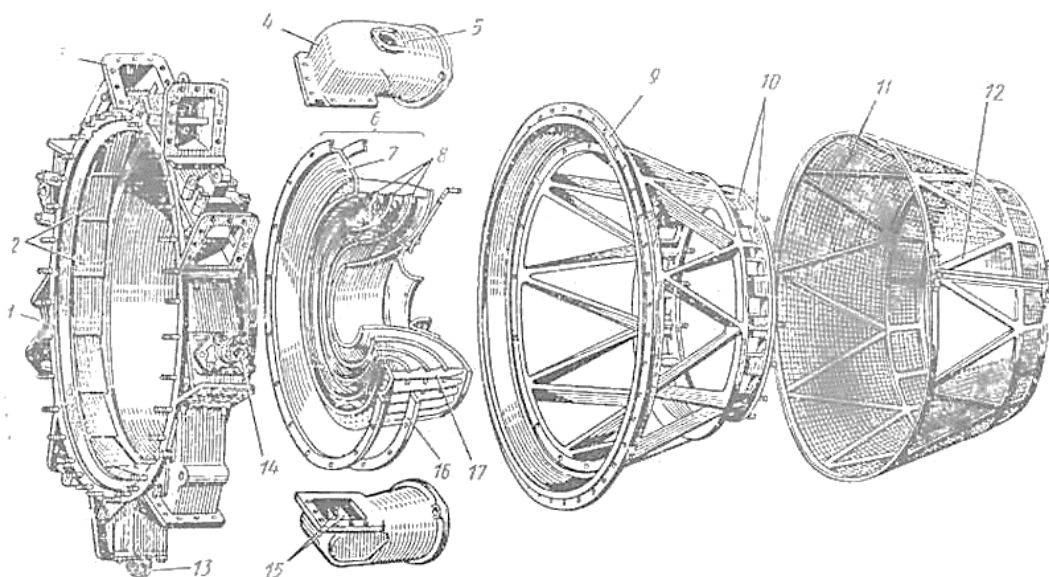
Детали корпуса центробежного компрессора: 1—корпус диффузора; 2—лопатки диффузора; 3 и 4—выходные патрубки; 5—фланец крепления топливной форсунки; 6—задний входной канал; 7—стенка входного канала; 8—разделительные кольца во входном канале; 9—задняя силовая ферма; 10—окна для подвода воздуха к колесу вентилятора; 11—защитная сетка; 12—каркас сетки; 13—нижняя опорная точка крепления; 14—одна из двухопорных цапф; 15—лопатки в выходном патрубке; 16—регулирующая прокладка; 17—лопатки неподвижного направляющего аппарата
